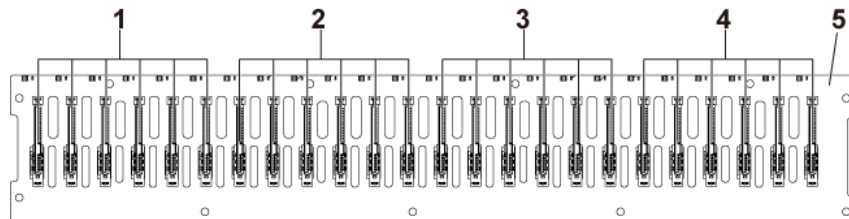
Vue arrière du fond de panier de disque dur de 2,5 pouces
